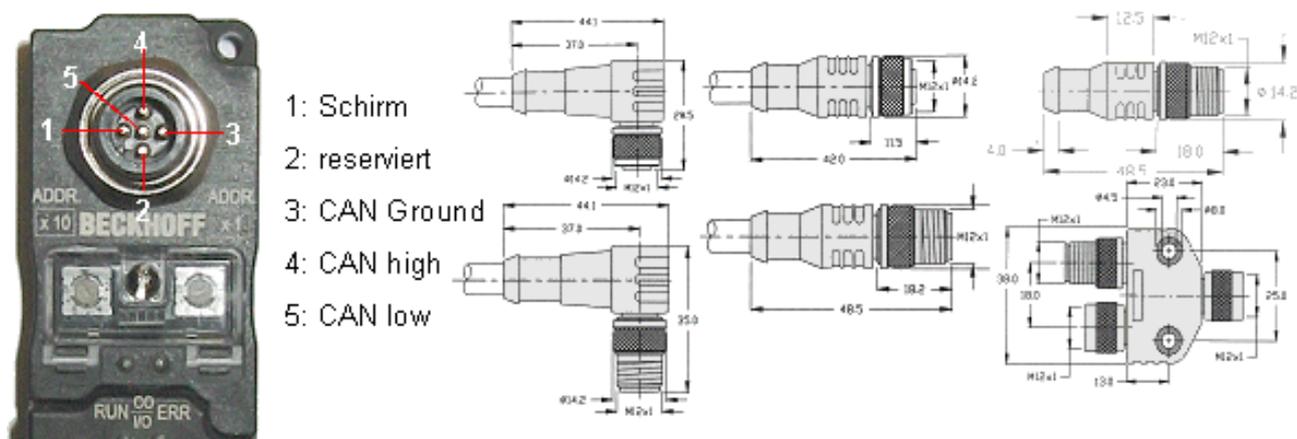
Pinbelegung M12 Stecker Feldbus Box
